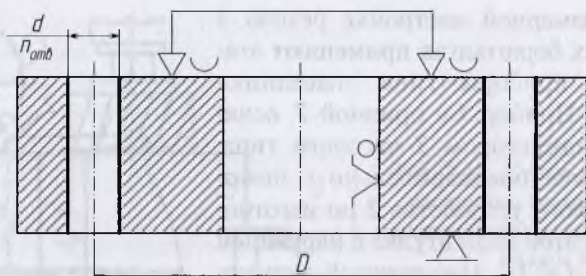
Схема установки заготовки на плоскость и цилиндрический палец
